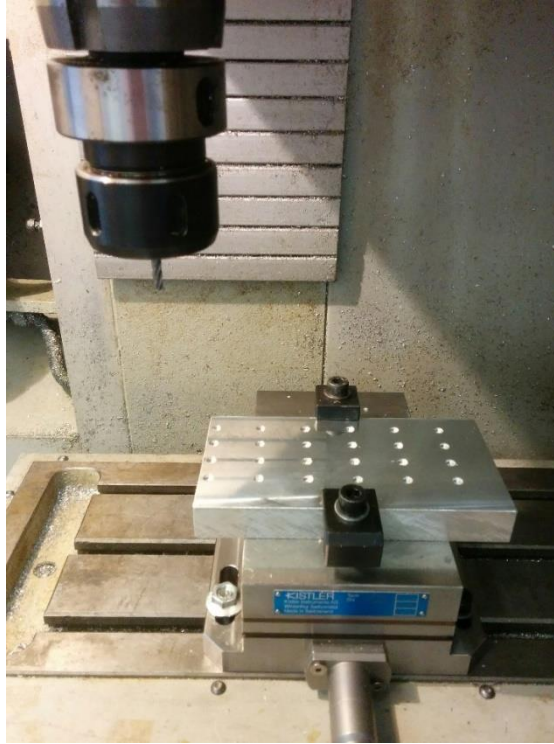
Disposición de experimentos en fresadora Odisea (4mm).
